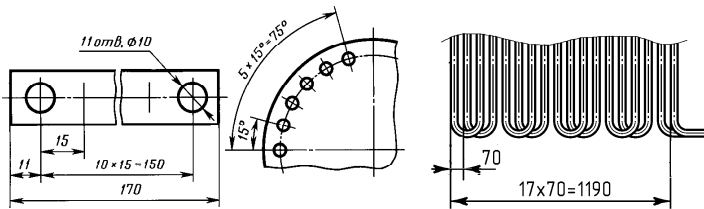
Нанесение размеров для равномерно расположенных элементов
